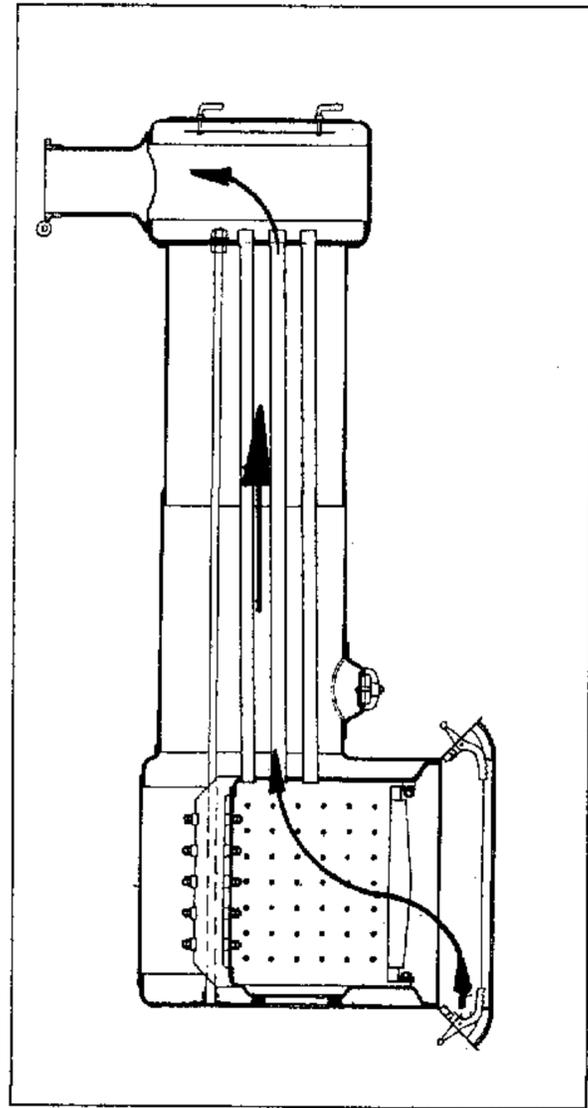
/2: Kessel mit „vorgehenden“ Rauchrohren für eine fahrbare Lokomotive (Maschinenfabrik Th. Flöther, 1912)
